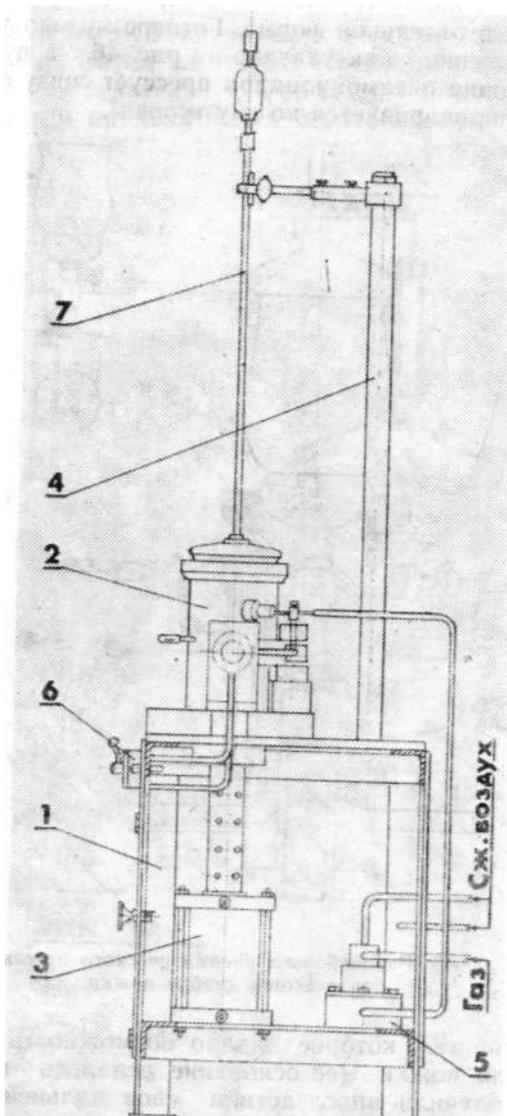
Одноместный пневматический пресс для подпрессовки ножки рюмки (общий вид).
